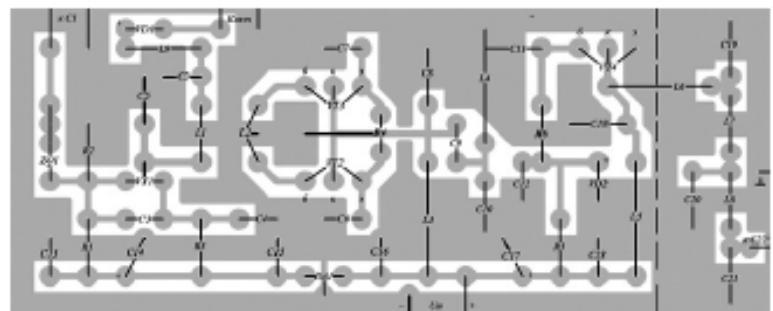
Эскиз монтажной платы CW-передатчика. Вид со стороны расположения деталей
